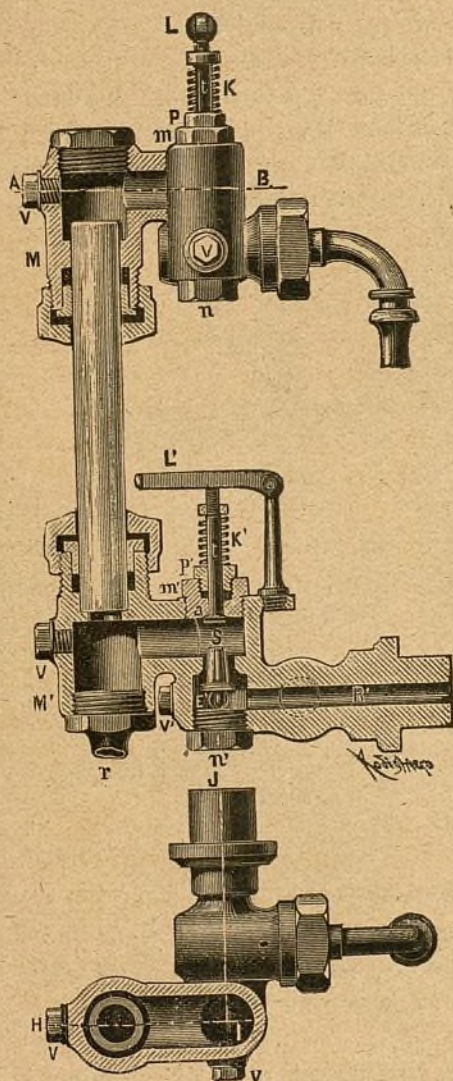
Nivel de agua con válvulas automáticas del constructor Sr. Baudouin.
